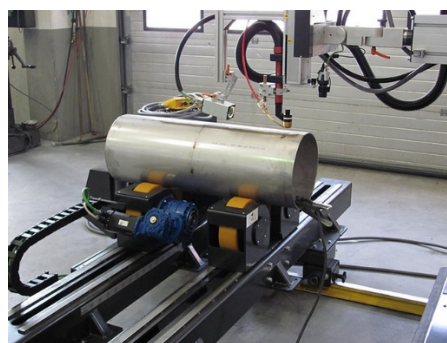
Soldadura circunferencial mecânica de juntas [47]
